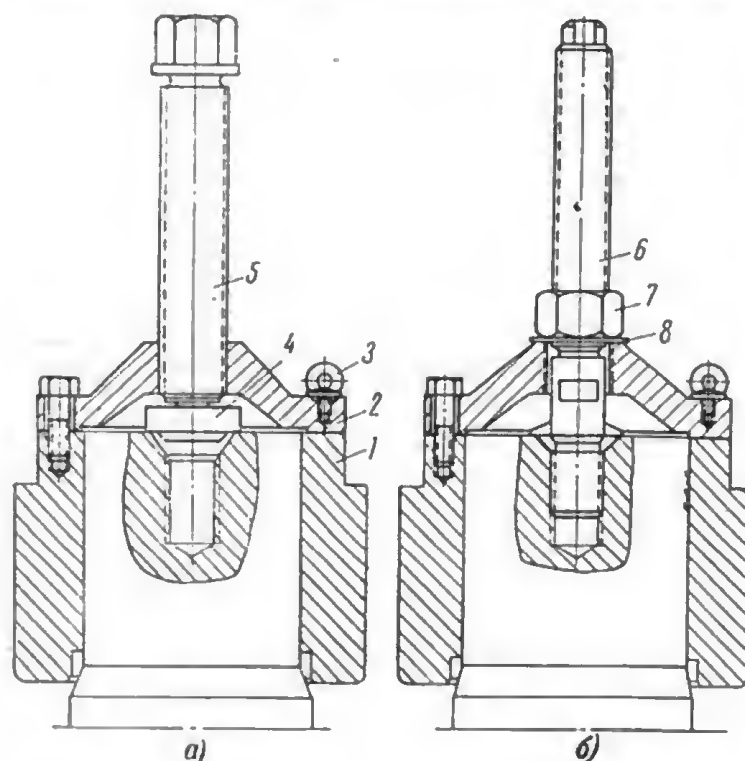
Приспособление для насадки и съема рычагов направляющих лопаток.
